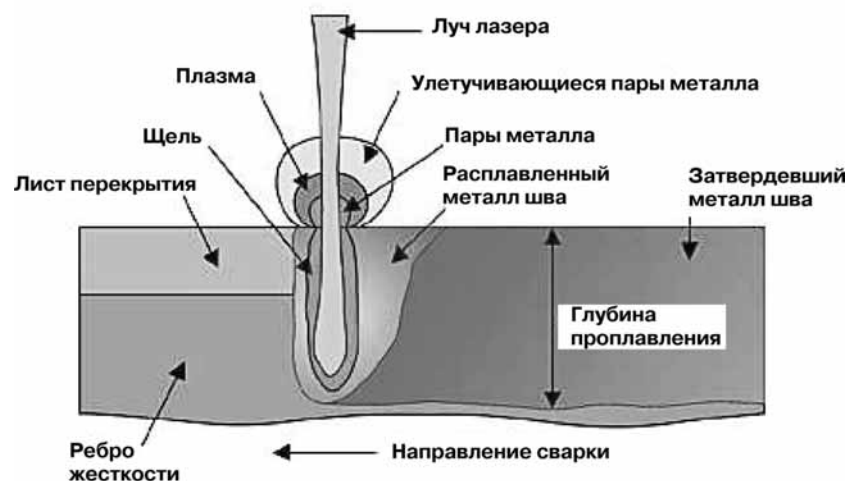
Схема процесса лазерной сварки сотовых панелей
